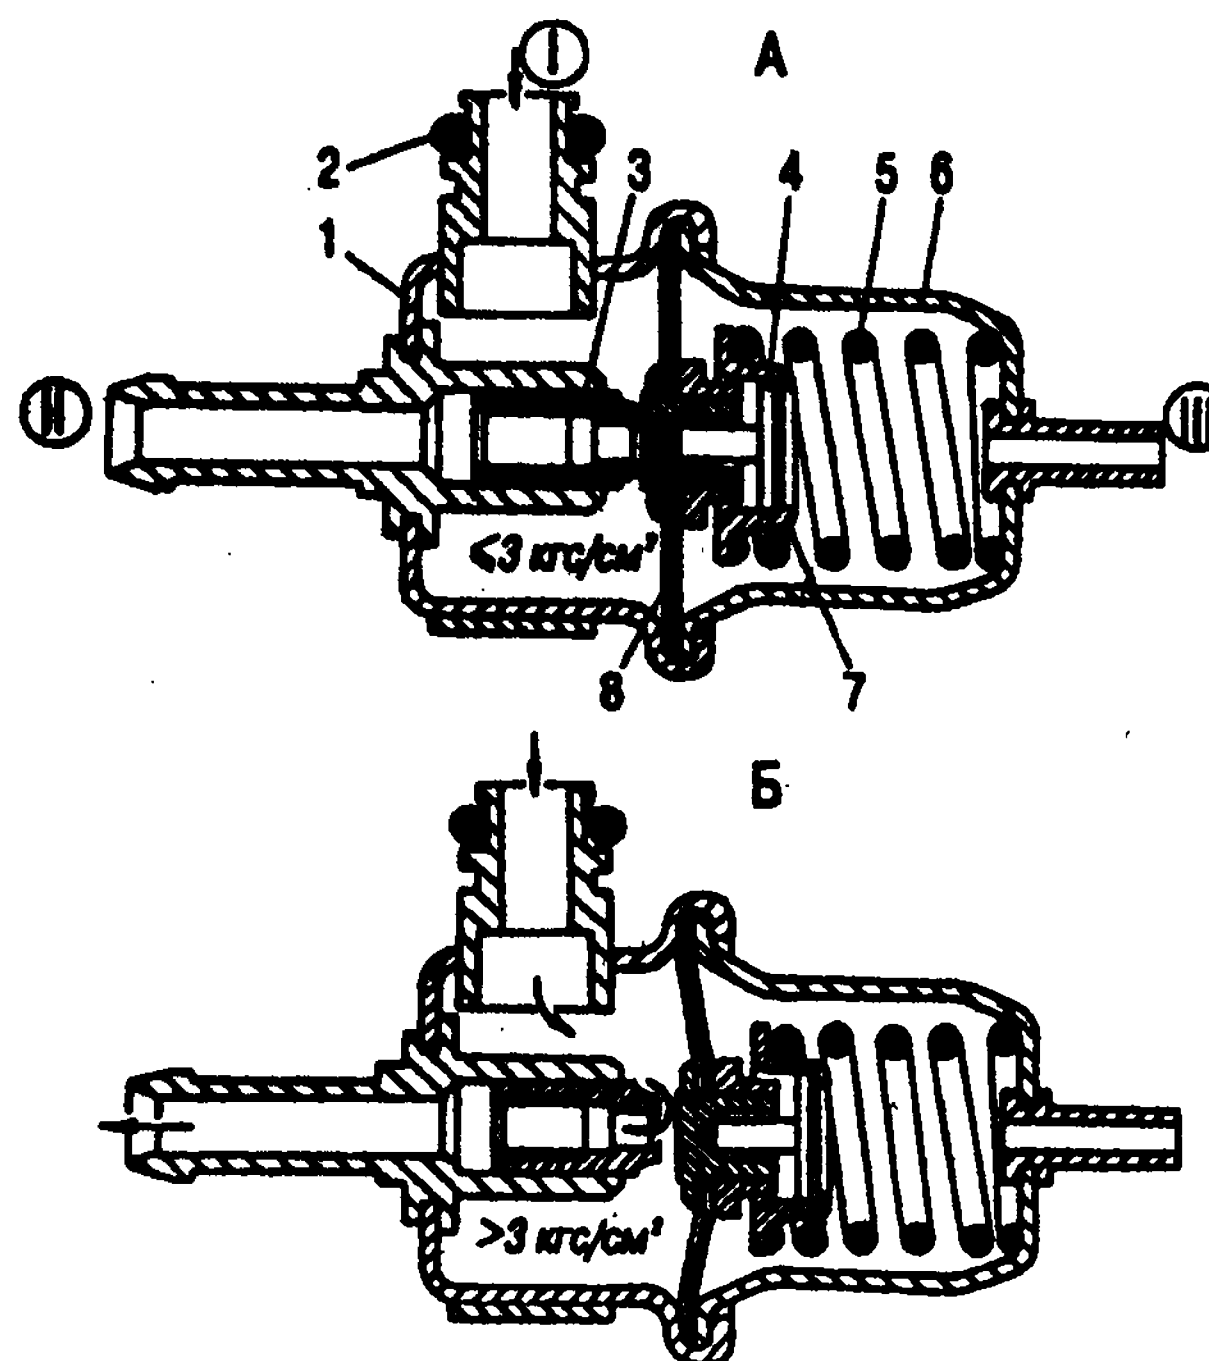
Регулятор давления топлива: 1 - корпус; 2 - резиновое кольцо; 3 - седло клапана; 4 - упор; 5 - пружина; 6 - крышка; 7 - тарелка пружины; 8 - диафрагма с клапаном; А - клапан закрыт; Б - клапан открыт; I - от топливопровода двигателя; II - к топливному баку; III - к ресиверу
